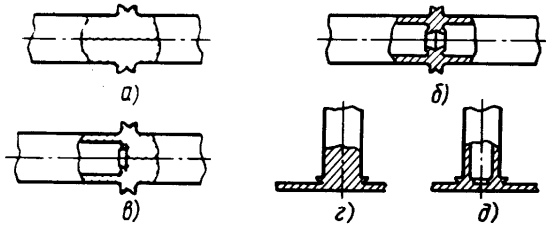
Типы сварных соединений, выполняемых при нагреве трением: а, б, в - стыковые; г, д - тавровые
